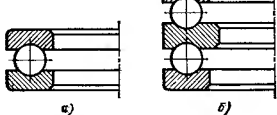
Шарикоподшипники упорные: а — одинарные; б — двойные
